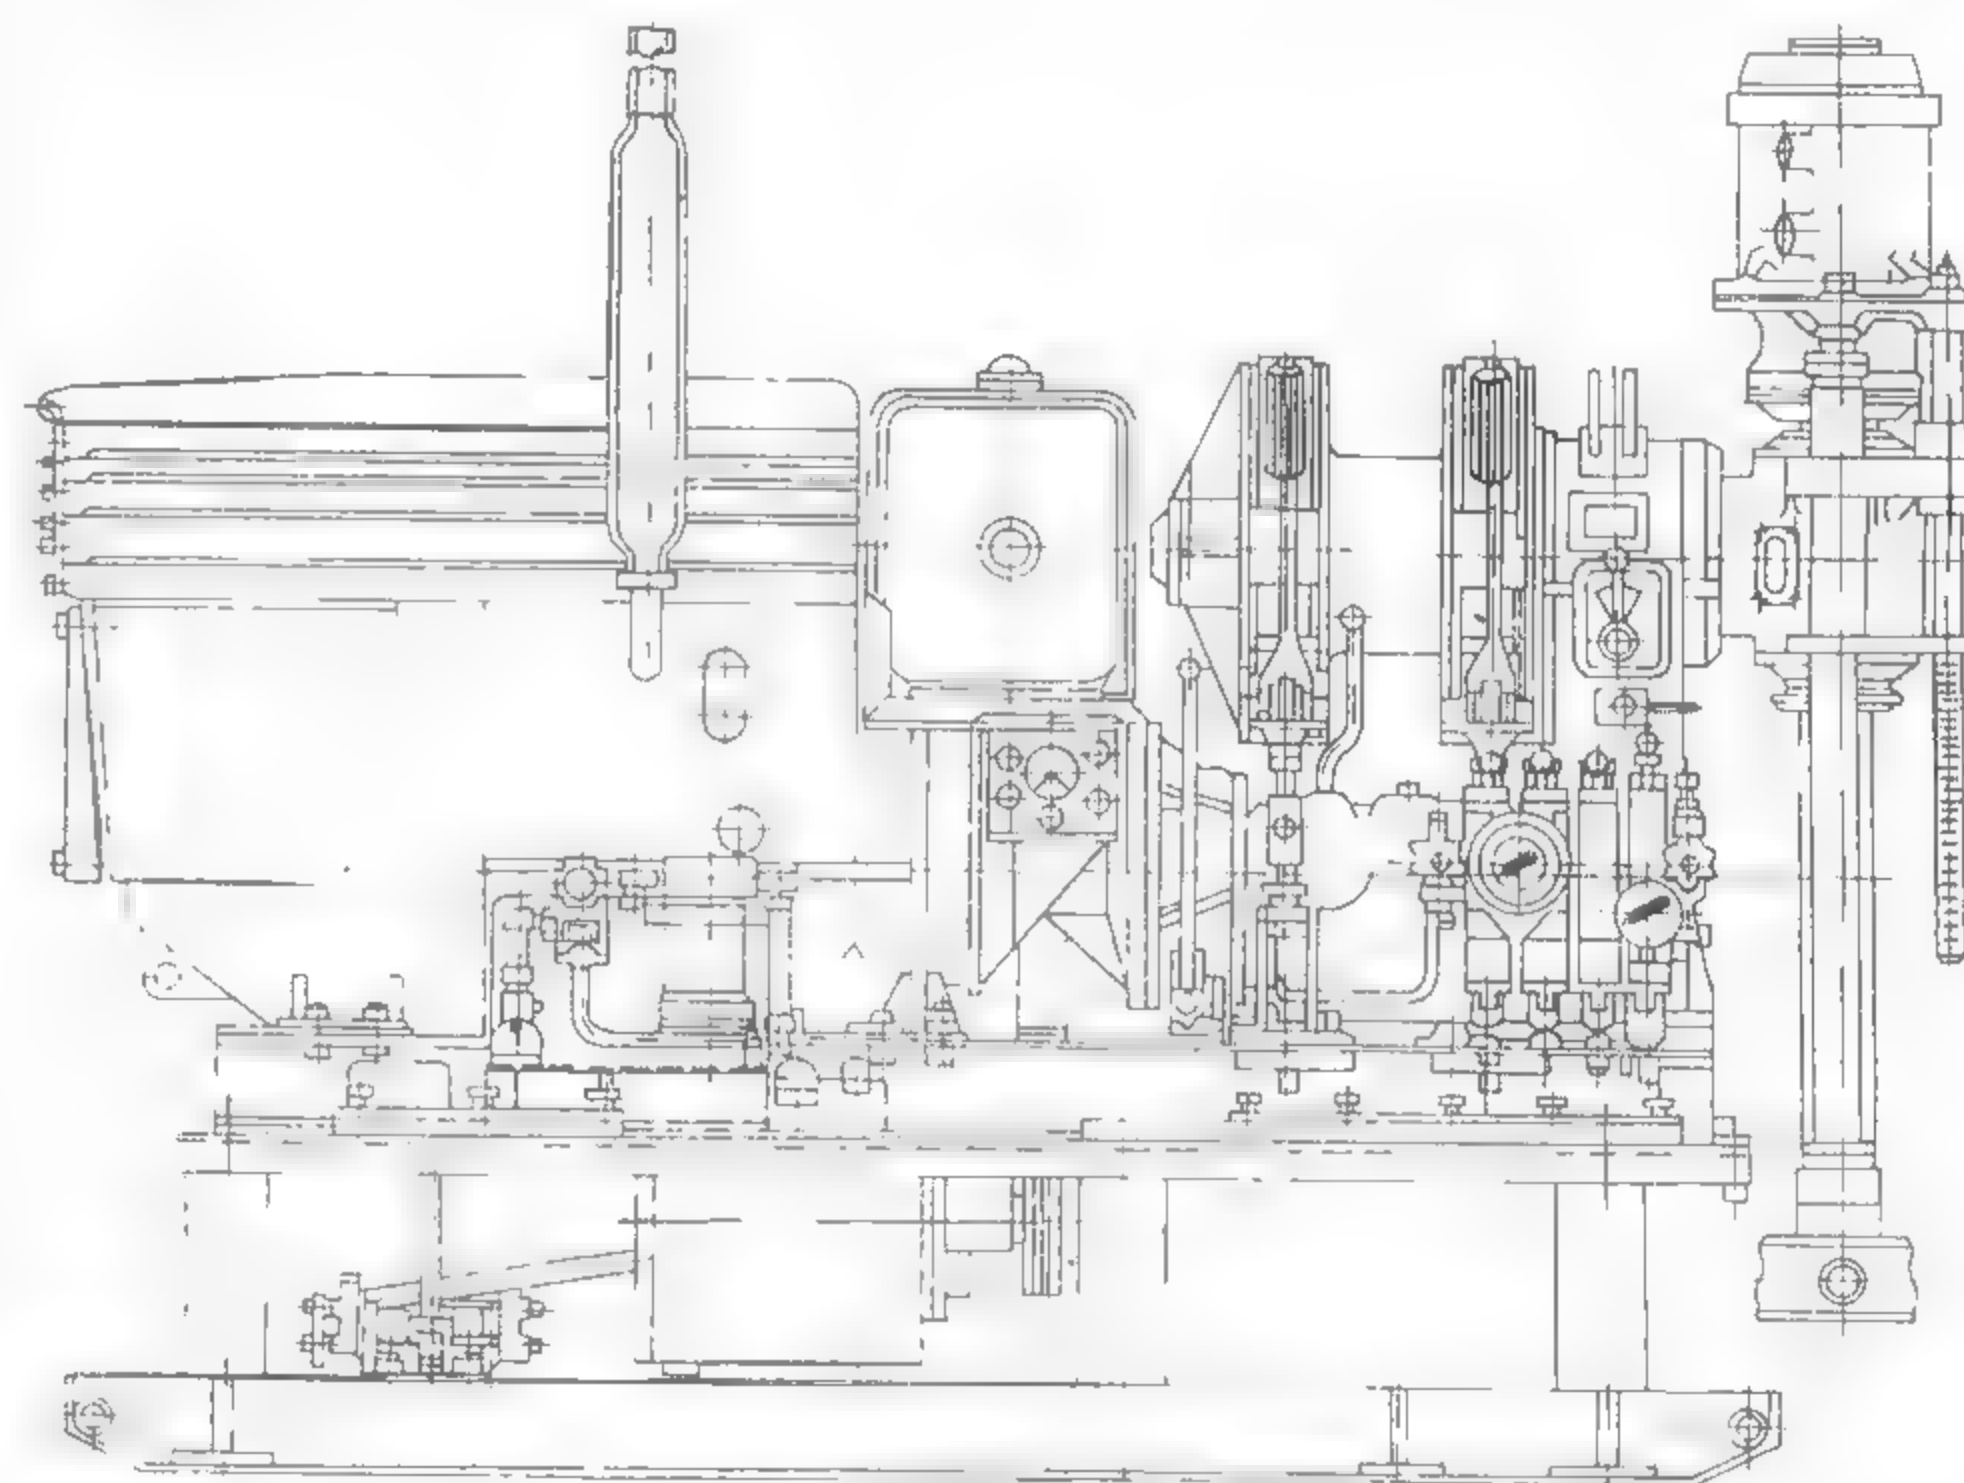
Grupul de foraj al instalației de foraj FG-8, acționat cu motor termic.
